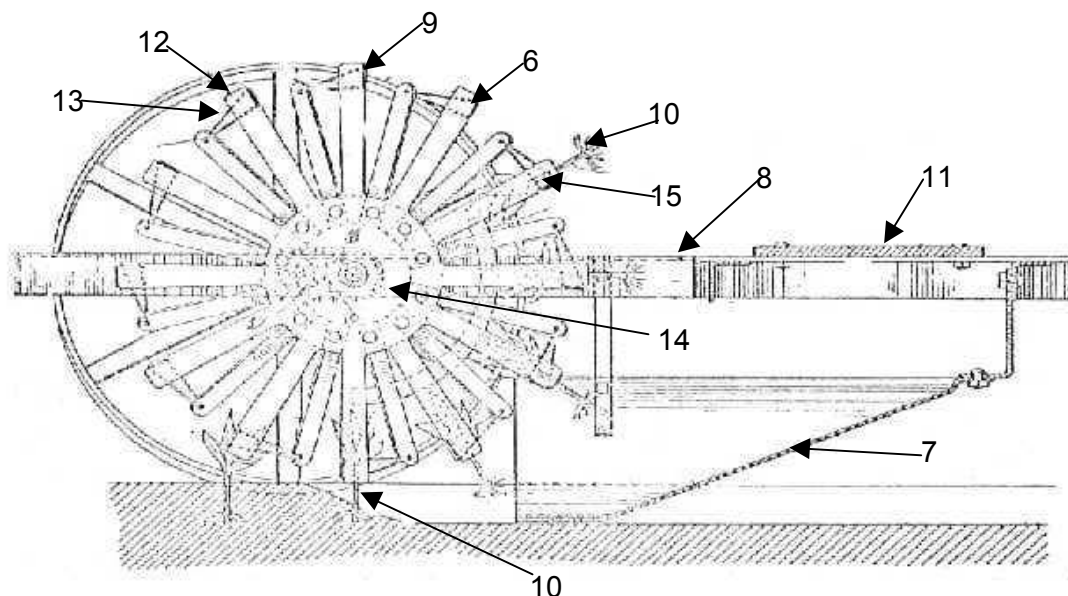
Detalhe do Conjunto Plantador (Patente 1888143)
